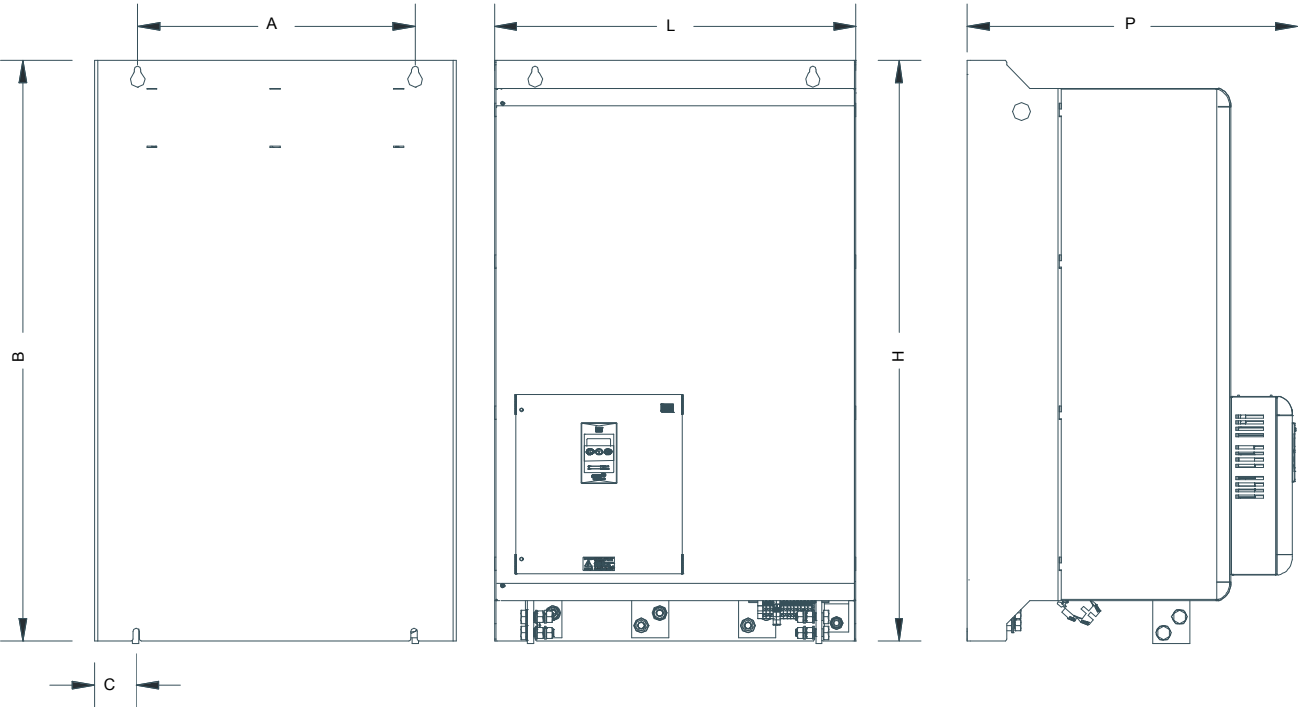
Dimensional do Conversor CTW-04 - Mec 06
